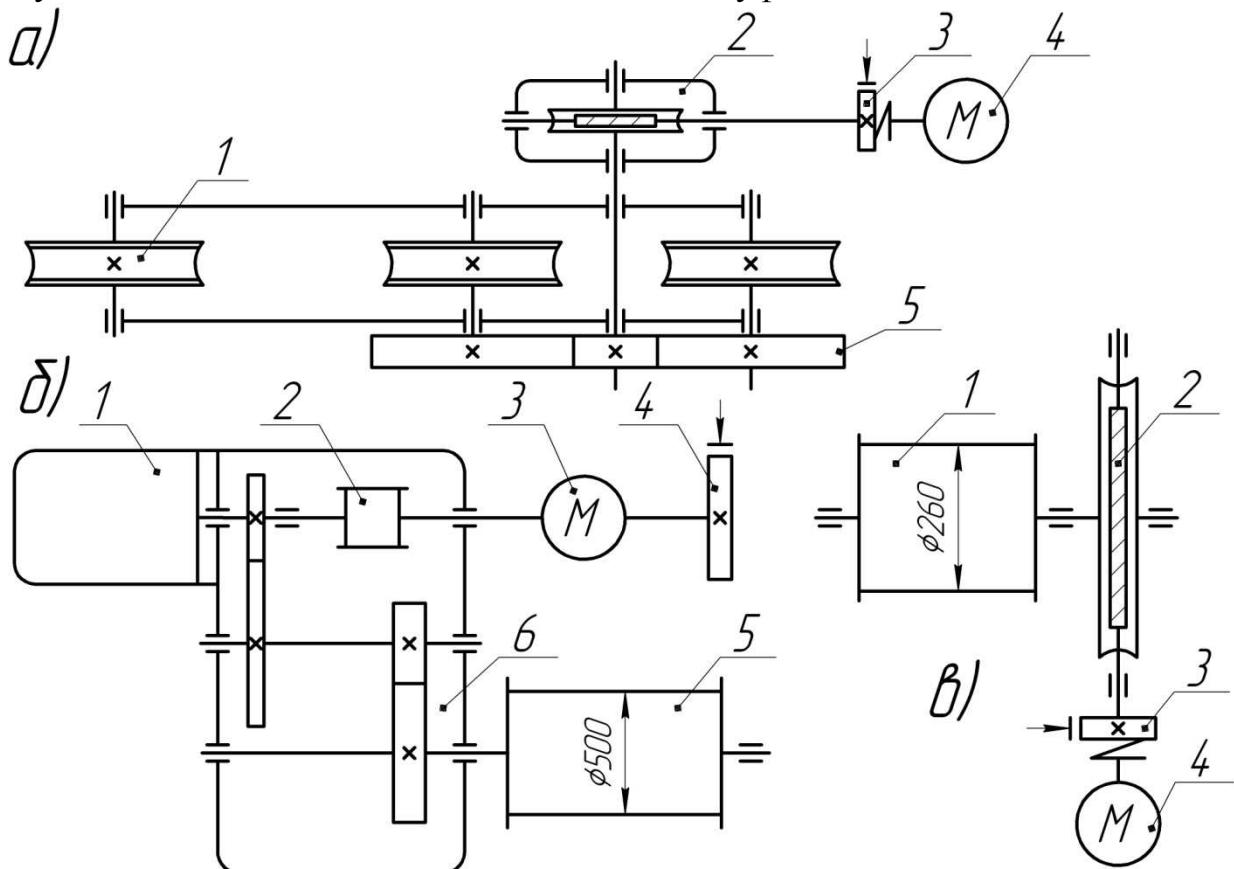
Кинематические схемы механизмов крана КБ-572: а – механизм передвижения приводной ходовой тележки, б – механизм подъёма груза, в – механизм передвижения грузовой тележки
